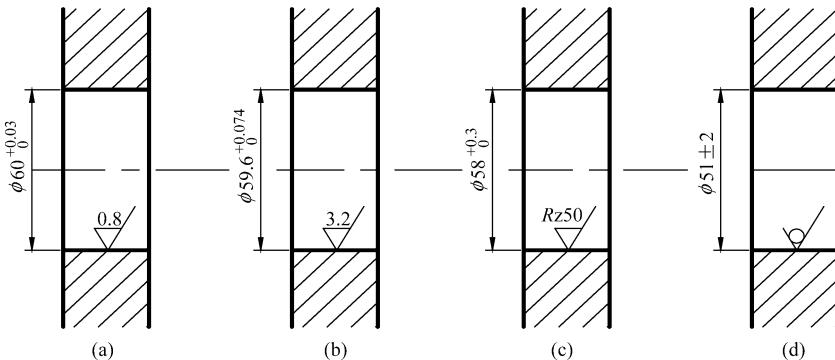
工艺基准与设计基准重合时工序尺寸及公差的计算实例
